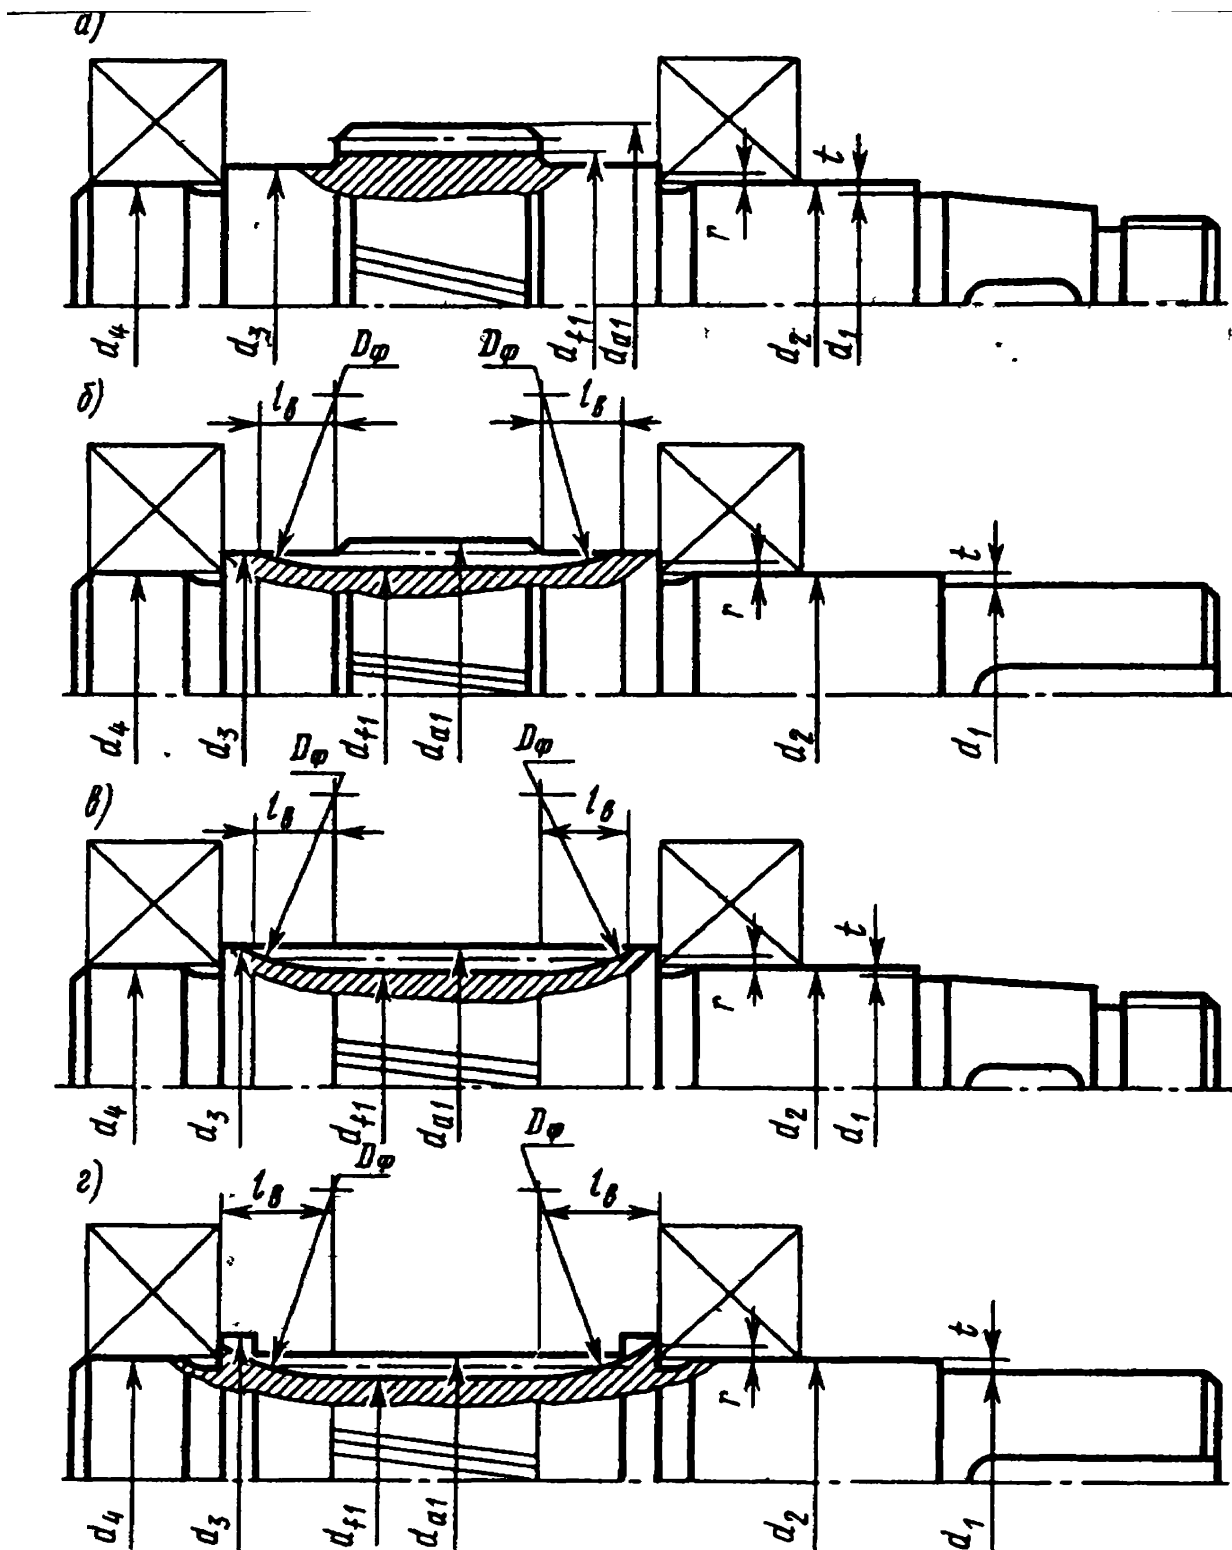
Конструкции вала-шестерни цилиндрической:
